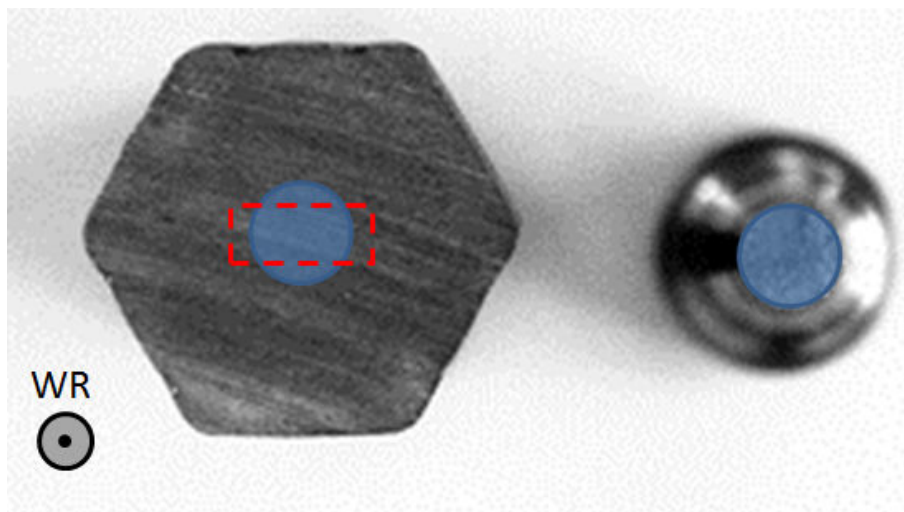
Probenlage im Querschnitt der Kaliberstäbe; blau: Zugprobenquerschnitt; rot: Gefügeprobe (Querschliff)
